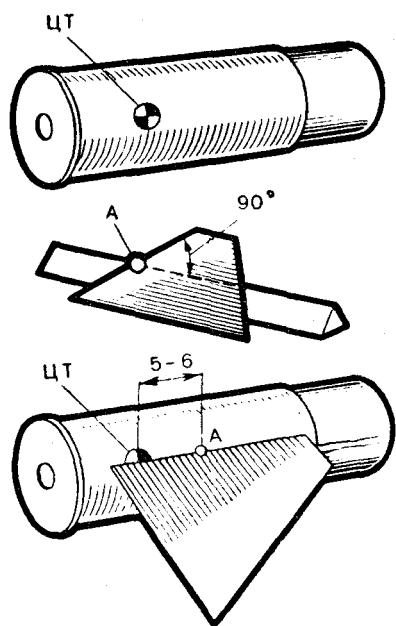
Установка стабилизаторов замедления спуска ступени.
